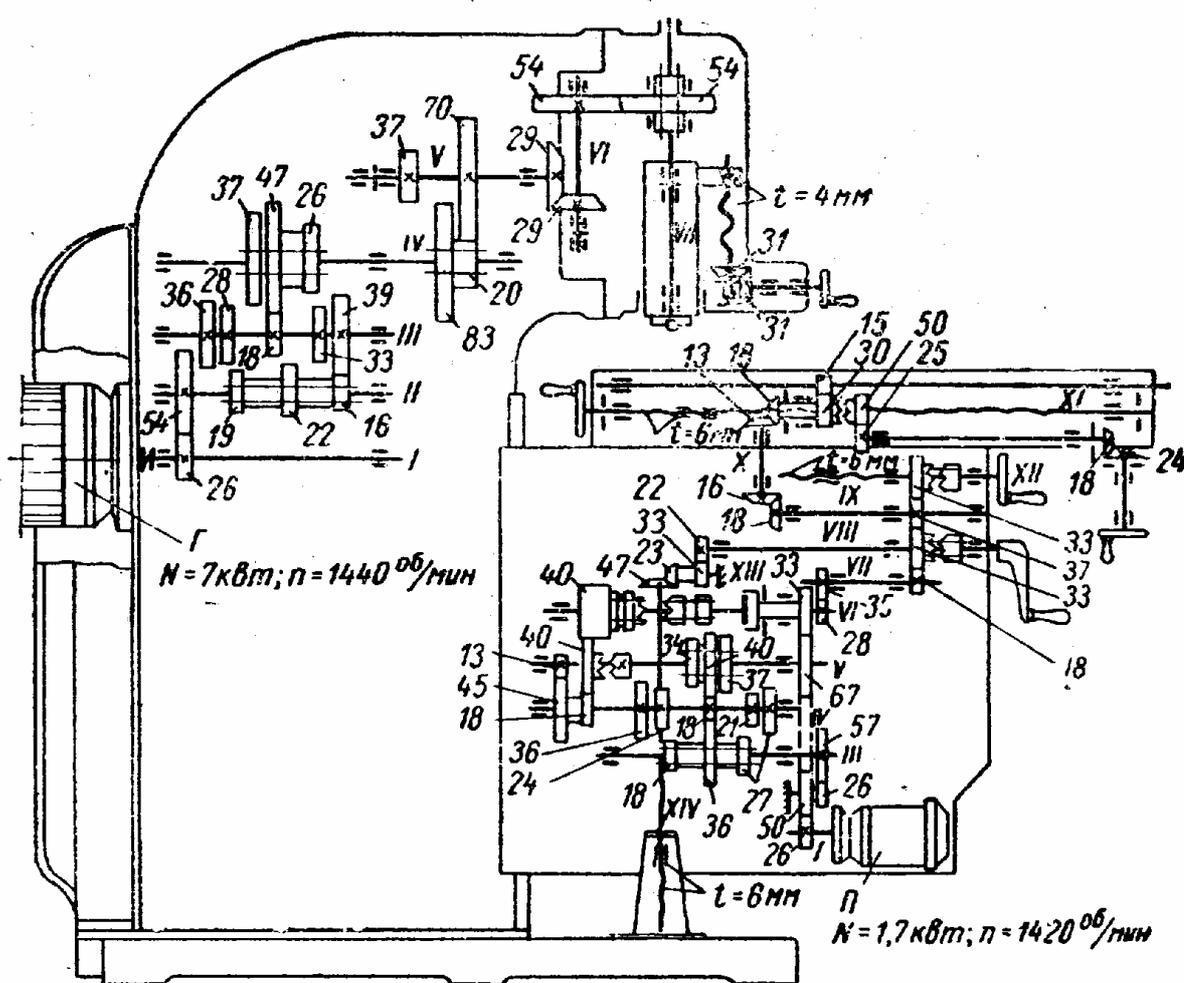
Кинематическая схема консольного вертикально-фрезерного станка 6М12П
